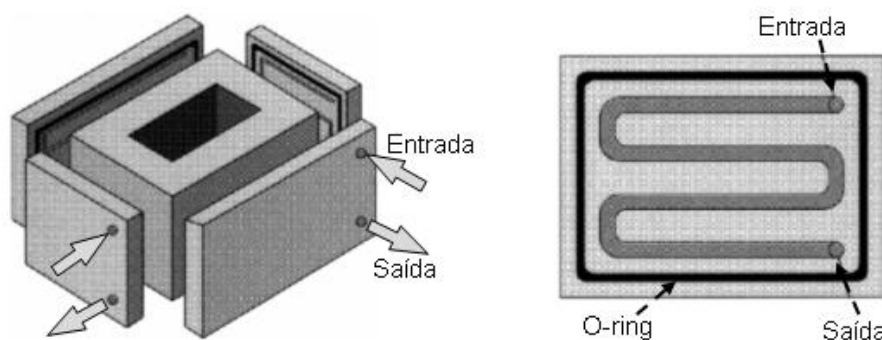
Sistema com canal usinado – Circuito "placas de refrigeração" (BRITO et al, 2004)
